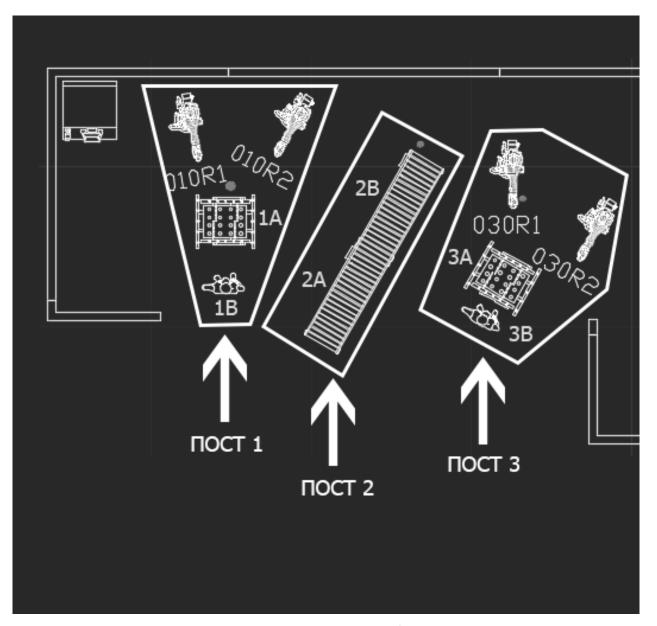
Линия сварки брызговика правого переднего крыла с лонжероном в сборе ВАЗ- $1118\,$
